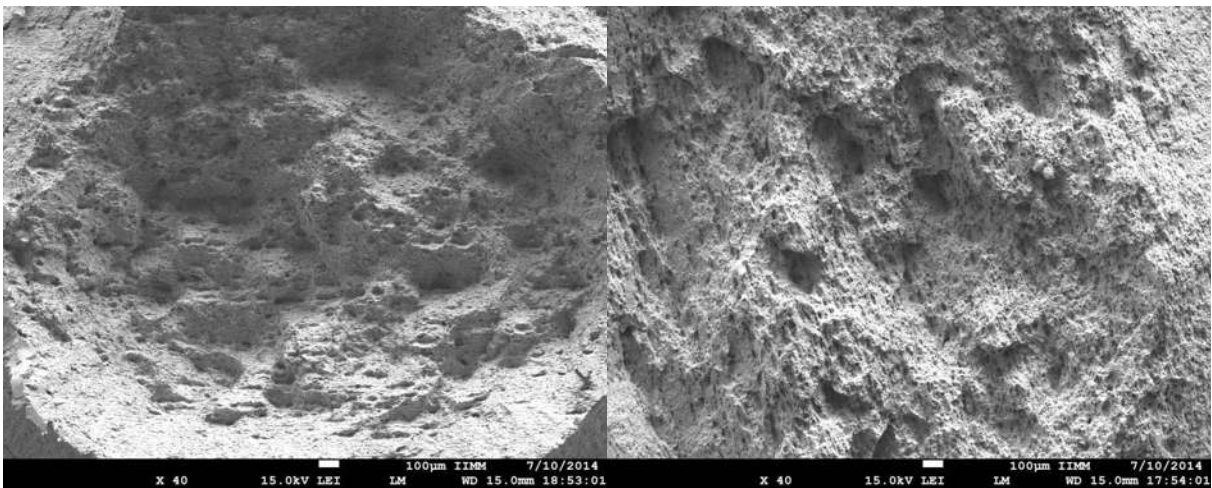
21.- Fractografía de la soldadura 3-1(cordón de auto-revenido, condición 1).
